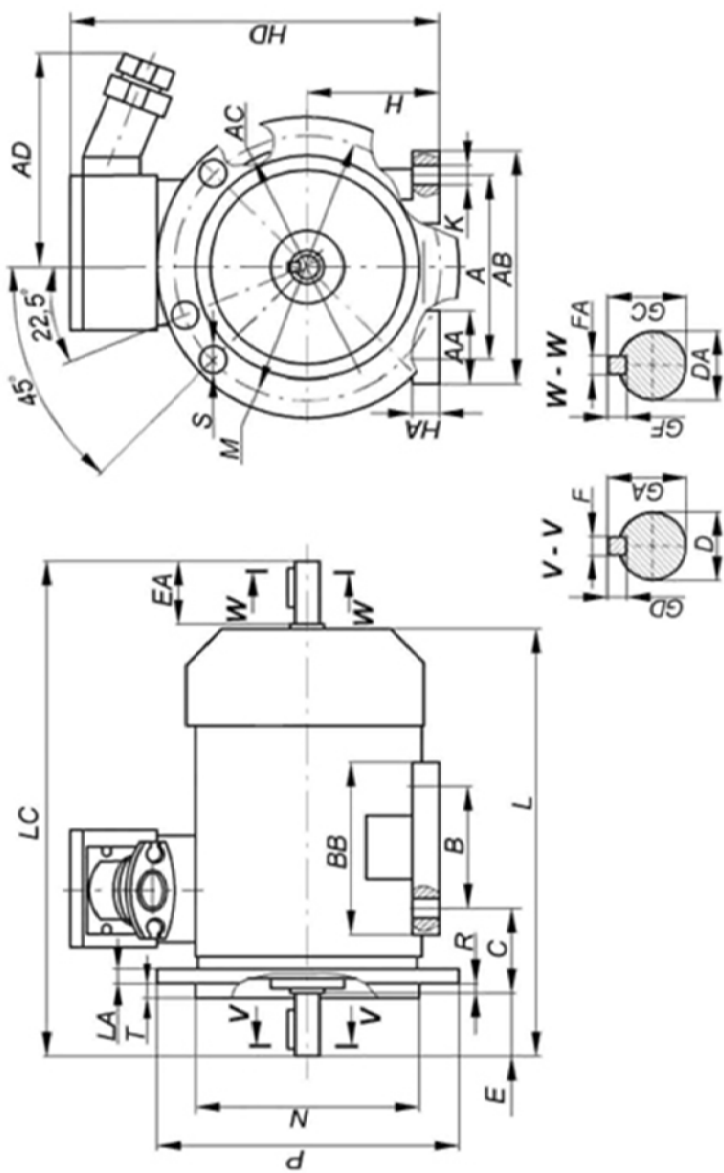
Габаритные, установочные и присоединительные размеры взрывозащищенных двигателей серии ВА. Монтажное исполнение [М 2...1, IM 2...2
